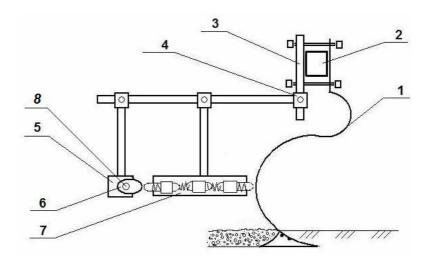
Предлагаемая схема виброударного рыхлителя почвы: 1 - упругая культиваторная стойка; 2 - рама культиватора; 3 - крепление; 4 - фиксатор положения; 5 - привод; 6 - кулачок; 7 - виброударный механизм; 8 - вал
